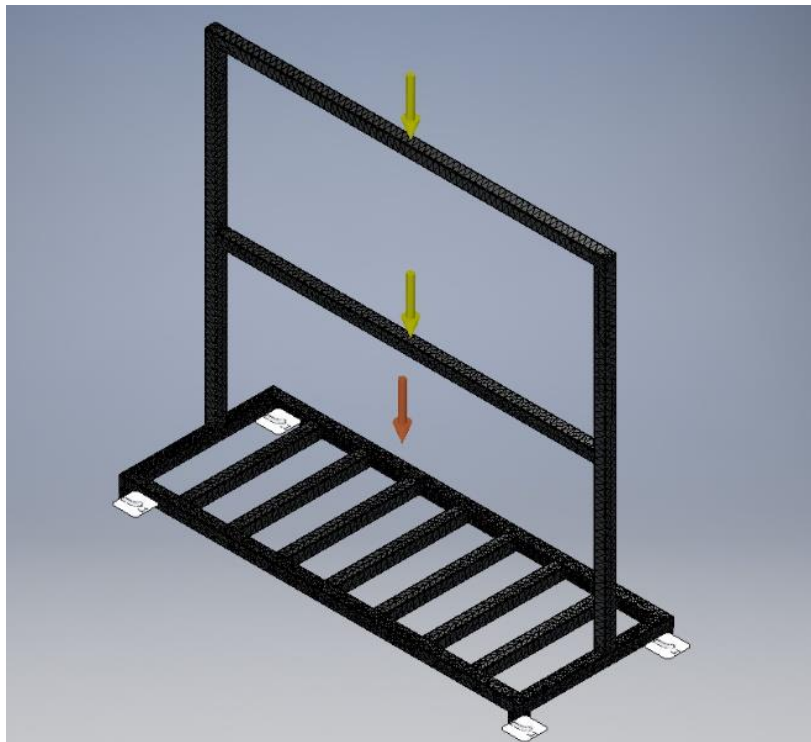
Mallado y fuerzas aplicadas a la estructura.
